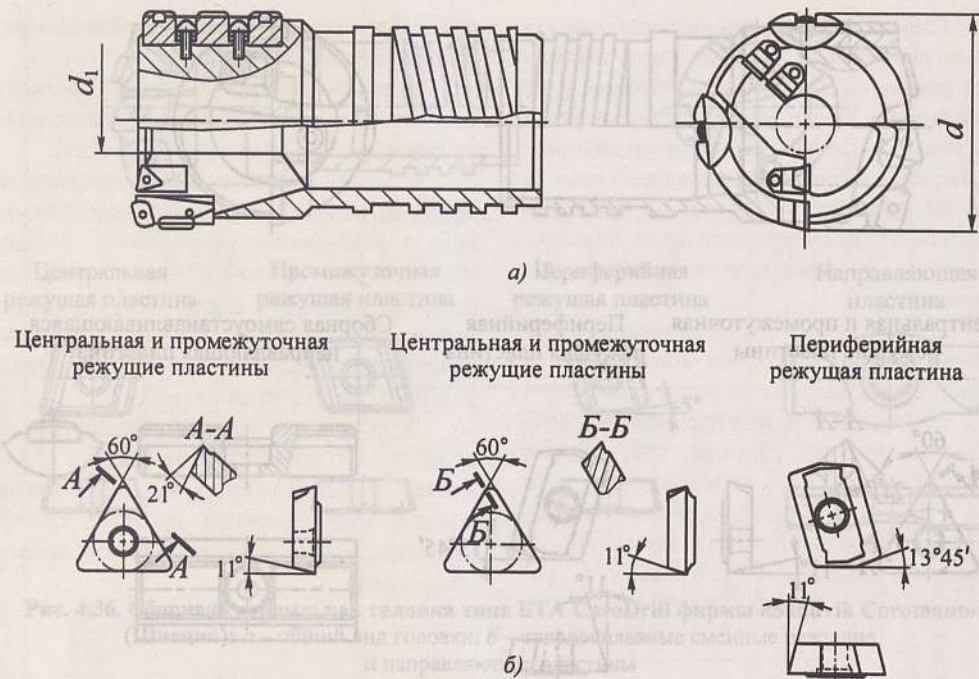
Сборная кольцевая сверлильная головка типа БТА фирмы «Sandvik Coromant»: а – общий вид головки; б – твердосплавные сменные режущие пластины
